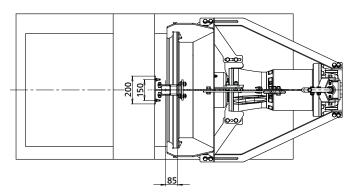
Dimensiones de Amaline 500, 600, 800 - material de la carcasa del motor: fundición gris
